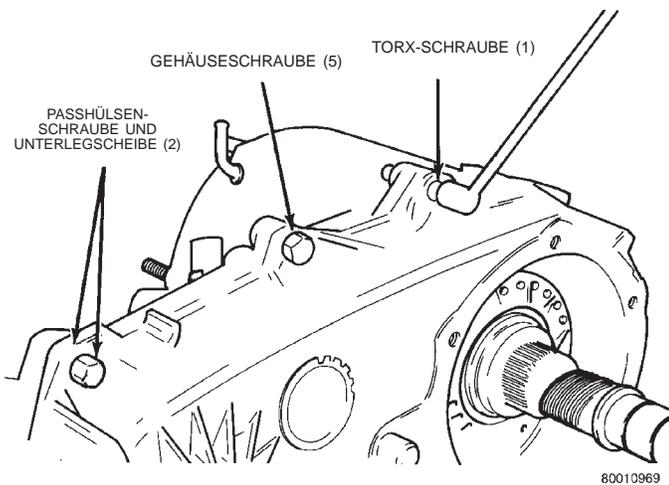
Paßhülzenschrauben an der hinteren Gehäusehälfte
